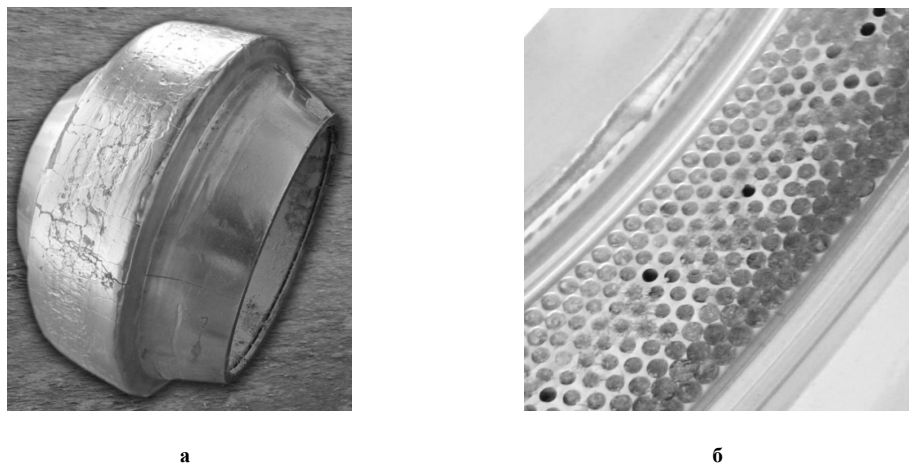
Зовнішній вигляд зношених робочих органів обладнання для виготовлення паливних гранул:
